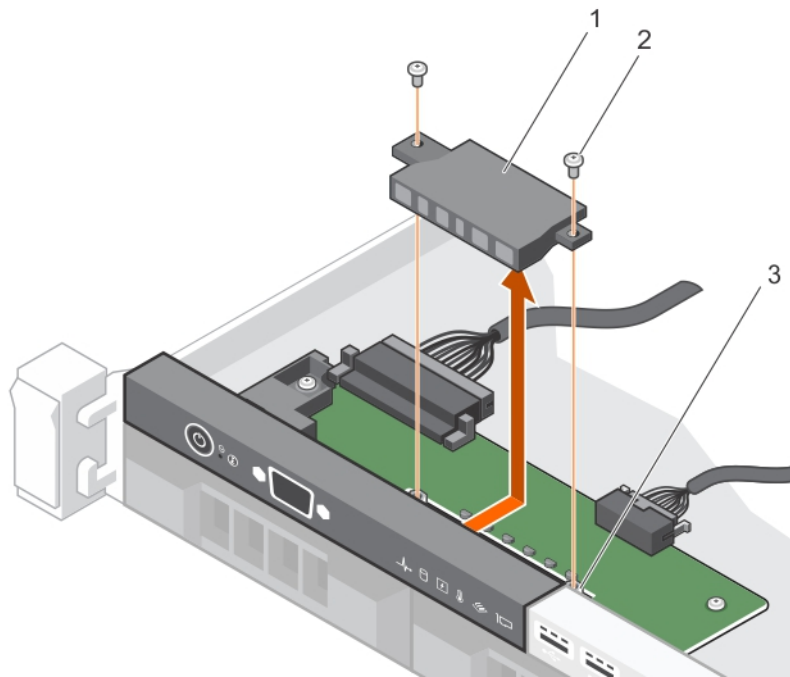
Installieren des LED-Moduls – Gehäuse für vier verkabelte Festplatten
